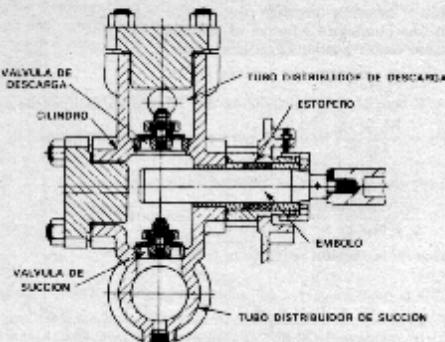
Extremo líquido de bomba horizontal. (Ingersoll-Rand Co.)
